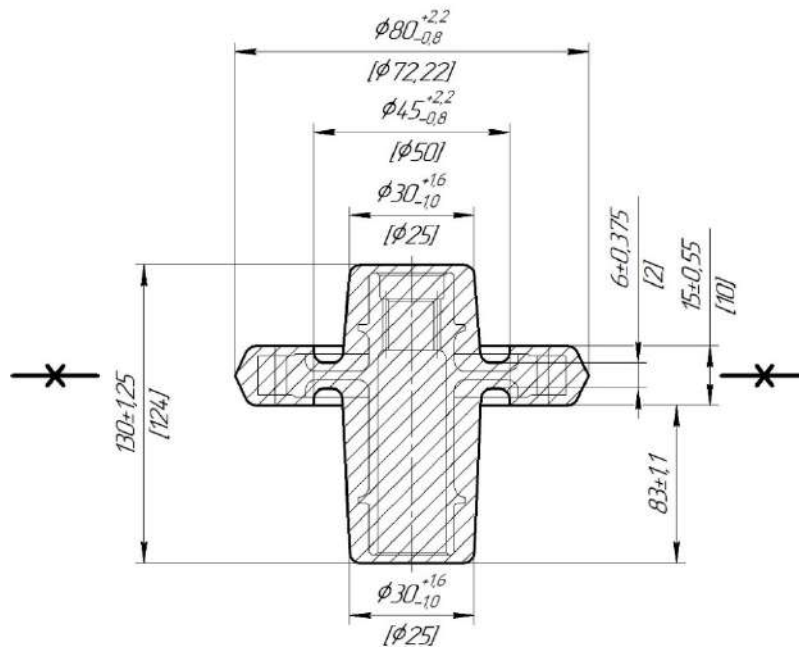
Ескіз заготовки, що отримана штамповкою на КГШП
